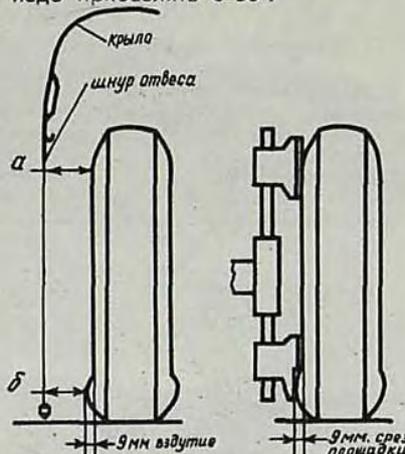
Замер развала колес при помощи отвеса (слева) и регулировка развала на стенде (справа).
